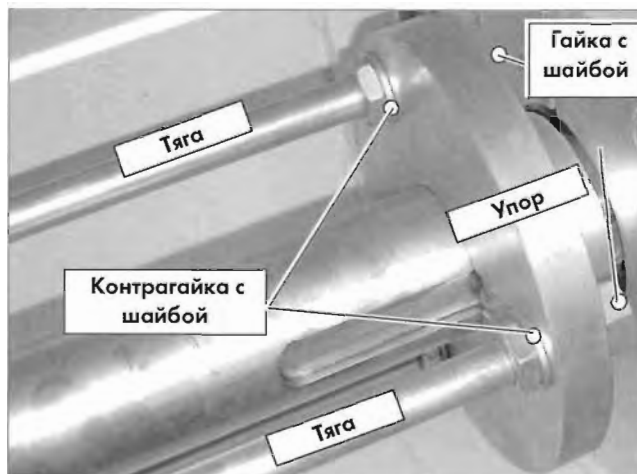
2 из 3 контрагаек, гаек, шайб и тяг на левом съемном подшипнике фрезерного вала
